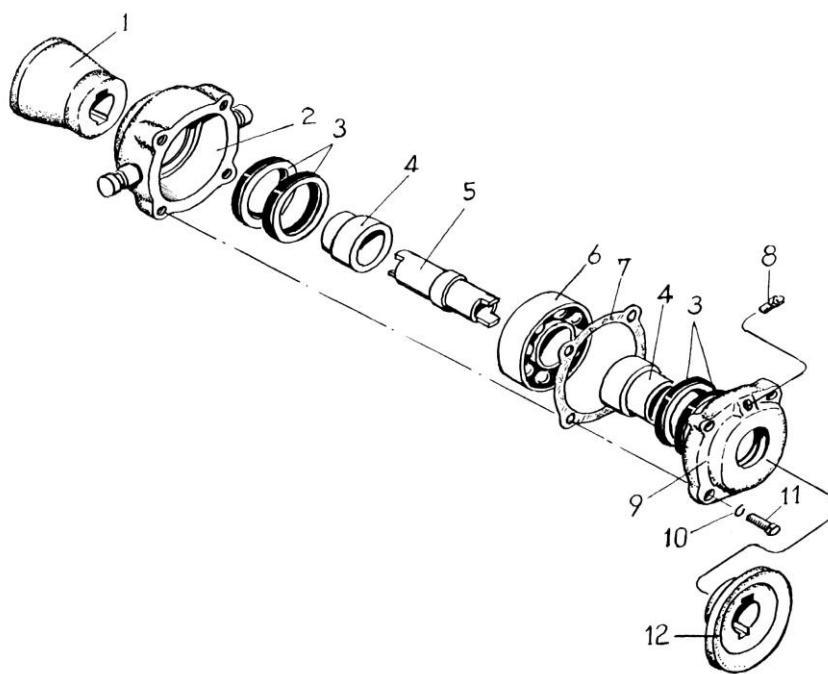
ПОДШИПНИК БАТАРЕИ БДТ 02.100-01
